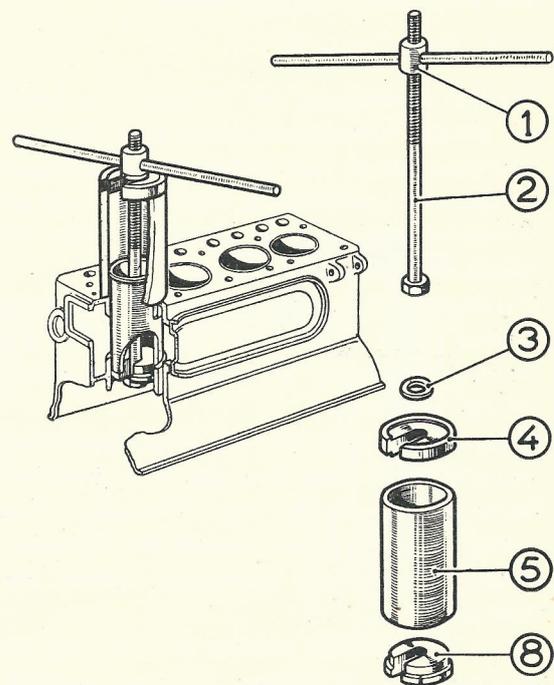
Typ 202. Demontage der Zylinderlaufbüchse.
